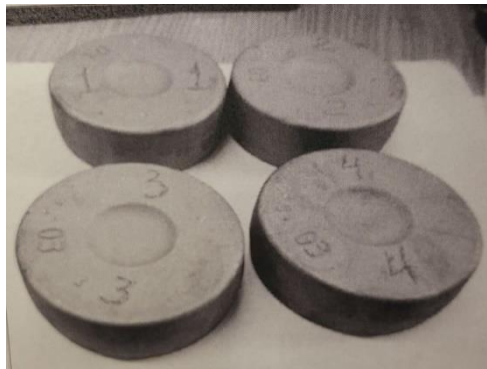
Зовнішній вигляд заготовок зі сталі ШХ15-Ш після штампування
